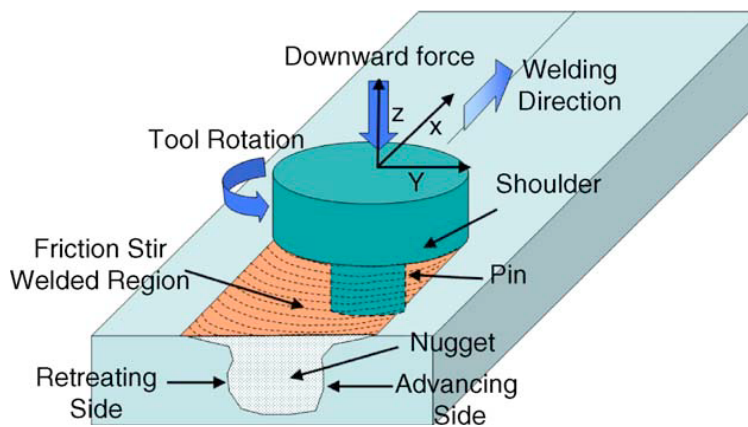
Esquema general del proceso de soldadura por fricción-agitación [2]
